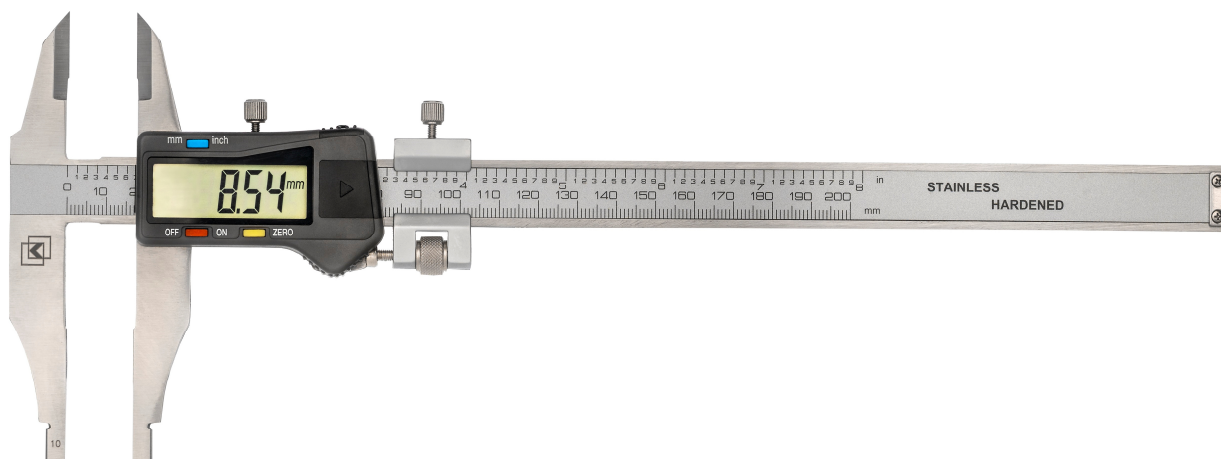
Общий вид штангенциркулей ШЦЦ-II
